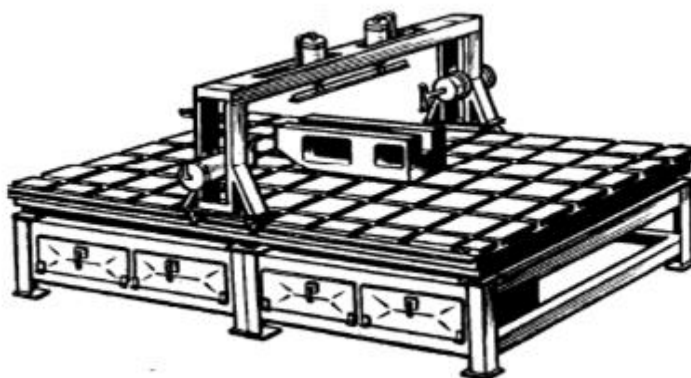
Универсальное сборочное приспособление для сварки (УСПС).
